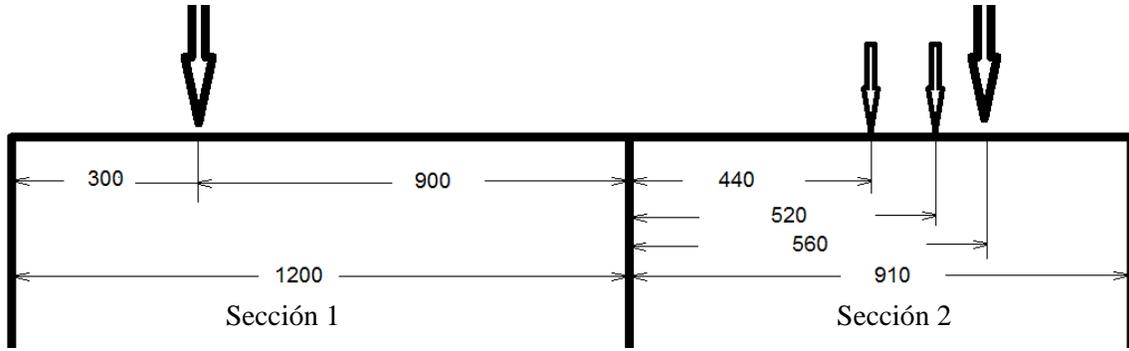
Diagrama de cargas en el soporte del sistema de sujeción. Fuente: Los autores.
